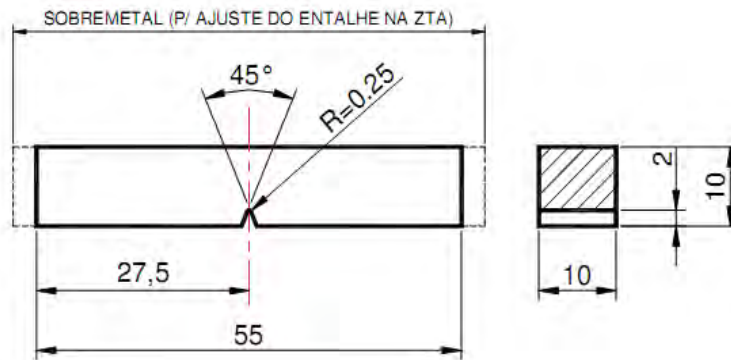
Configuração geométrica e dimensional dos corpos-de-prova de impacto Charpy-V.
